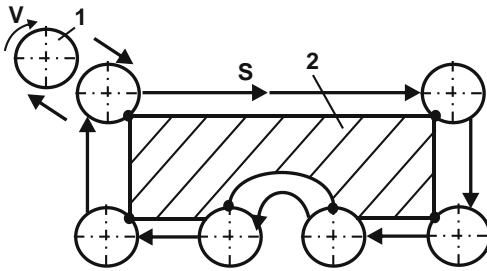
Схема обробки кінцевою фрезою 1 плоскої деталі 2 на верстаті з ЧПУ
